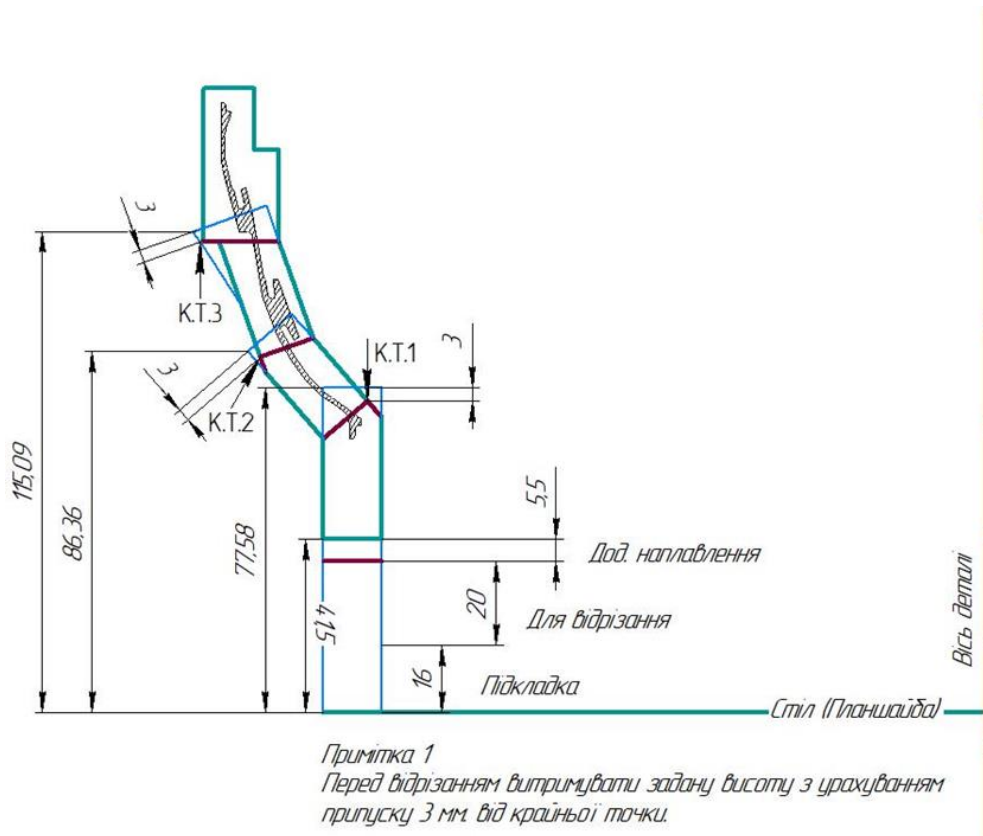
Креслення контрольних точок наплавлення деталі 4500301001
